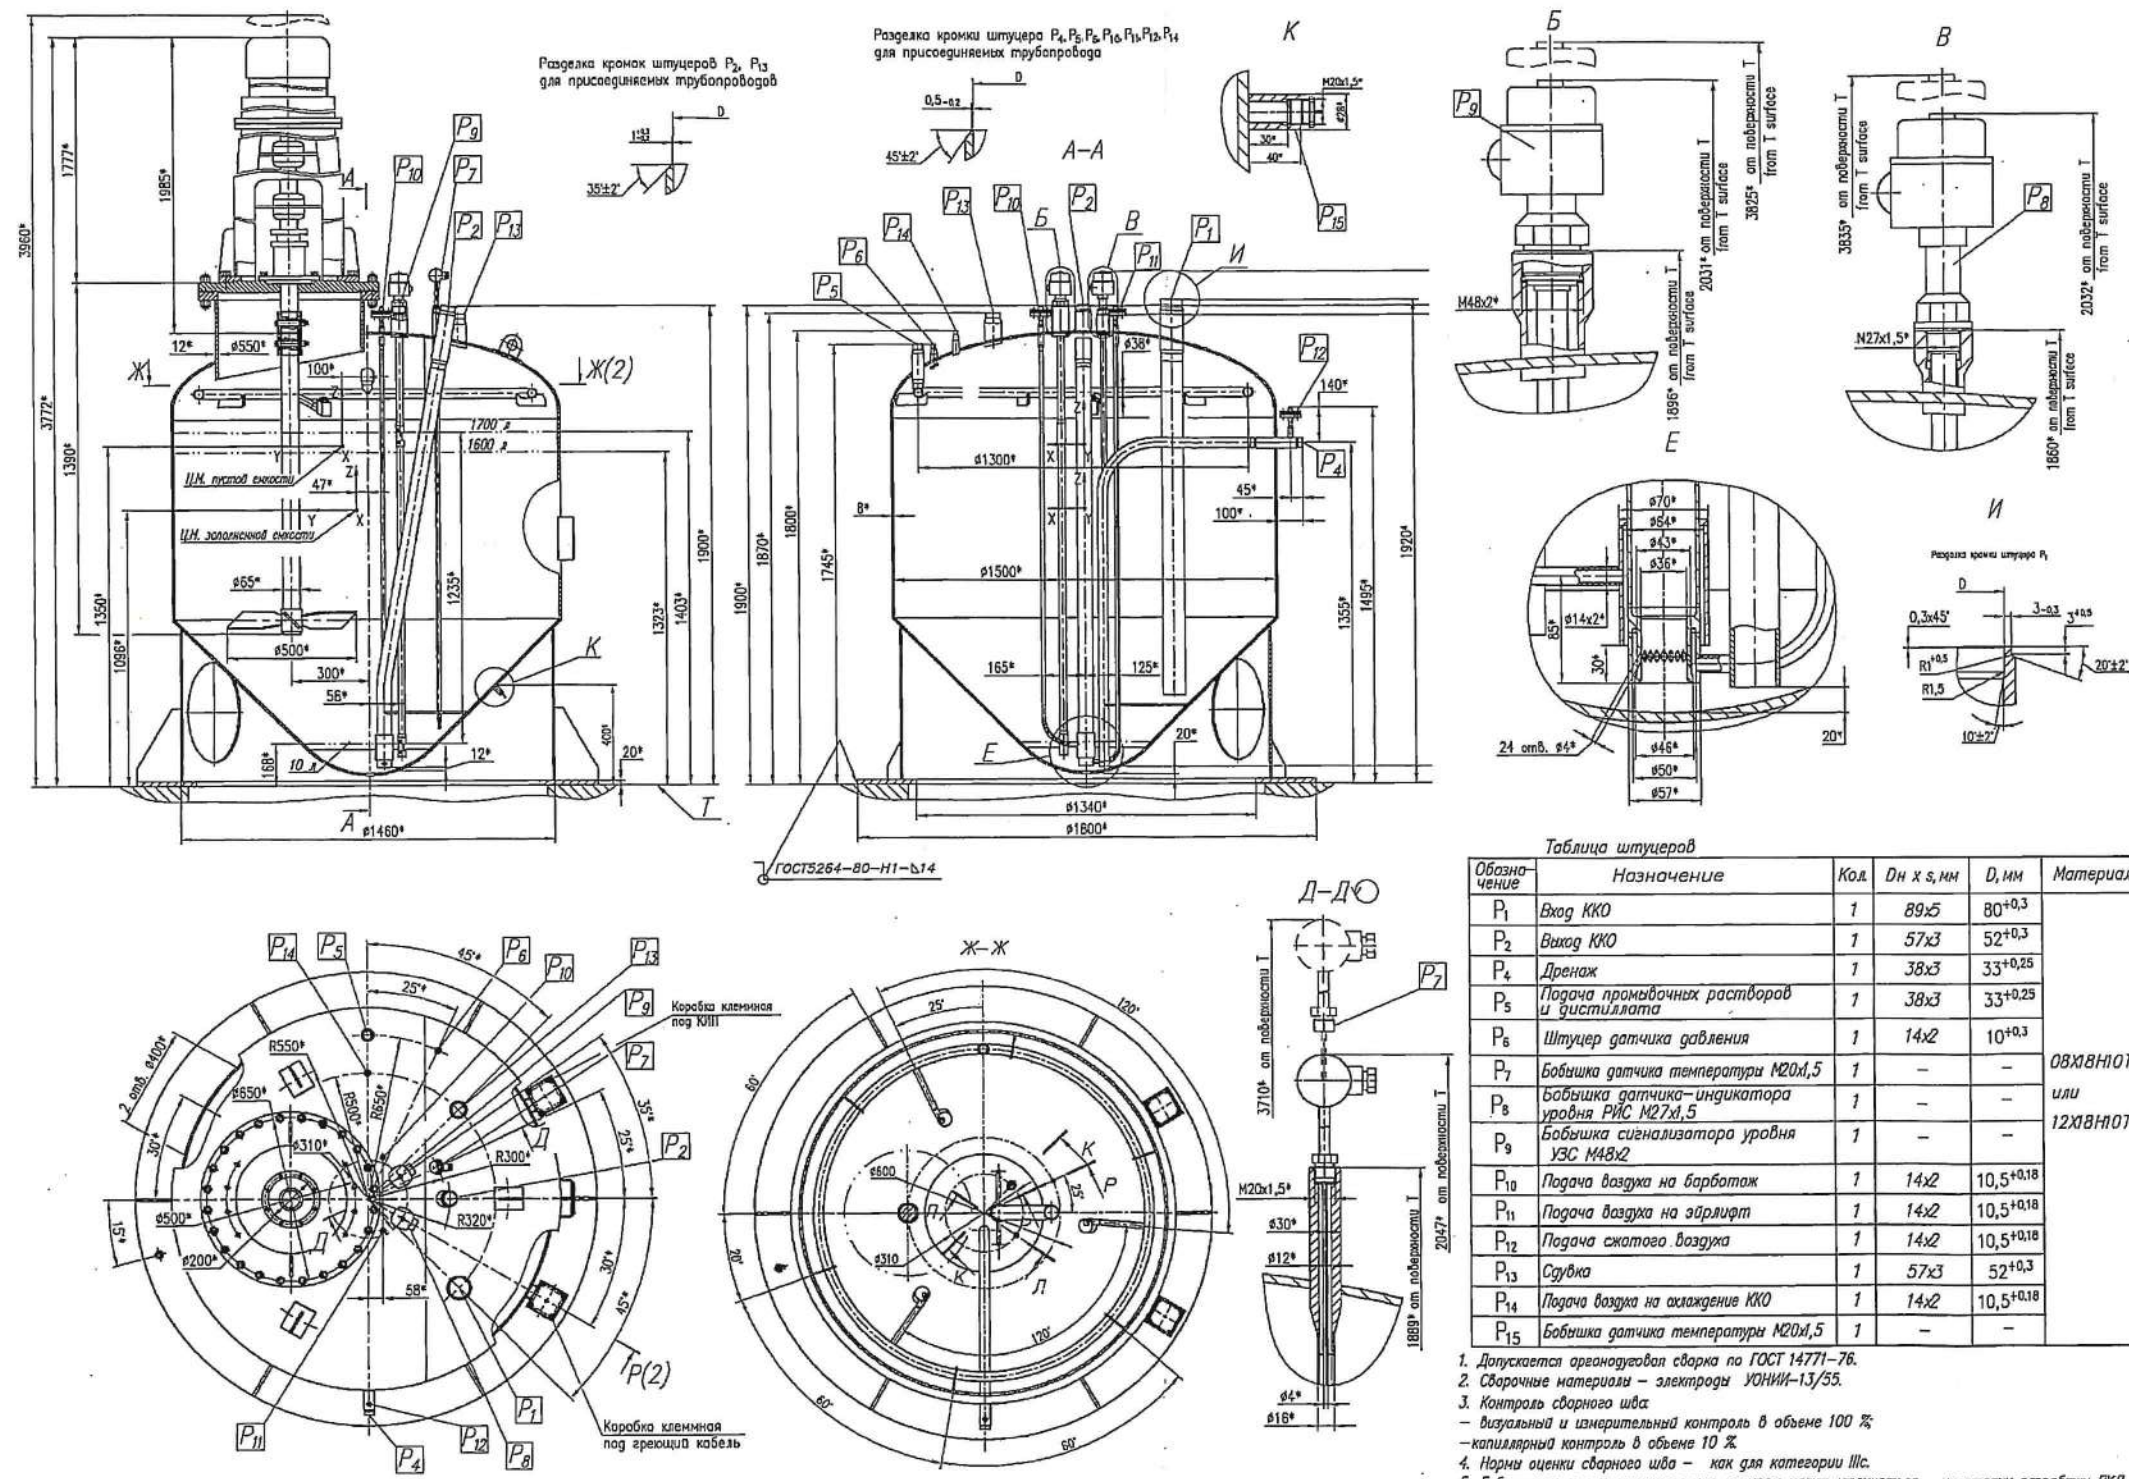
Габаритные, присоединительные размеры и конструктивное устройство емкости
